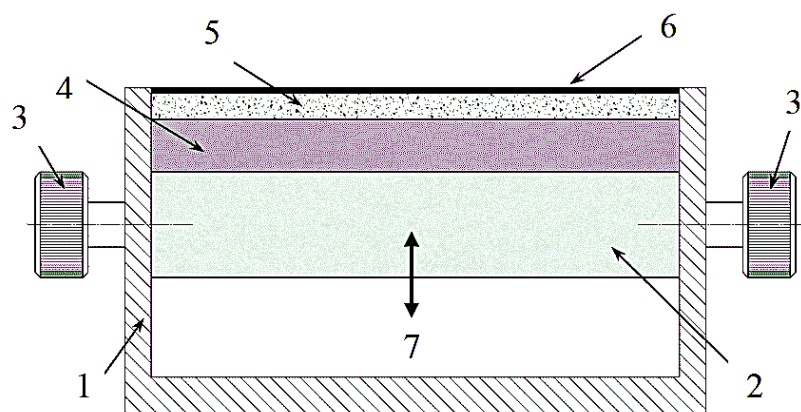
Оснащення для наплавлення: 1 – корпус; 2 – платформа; 3 – гвинт; 4 – підкладка; 5 – виріб; 6 – шар порошку; 7 – напрямок переміщення платформи
